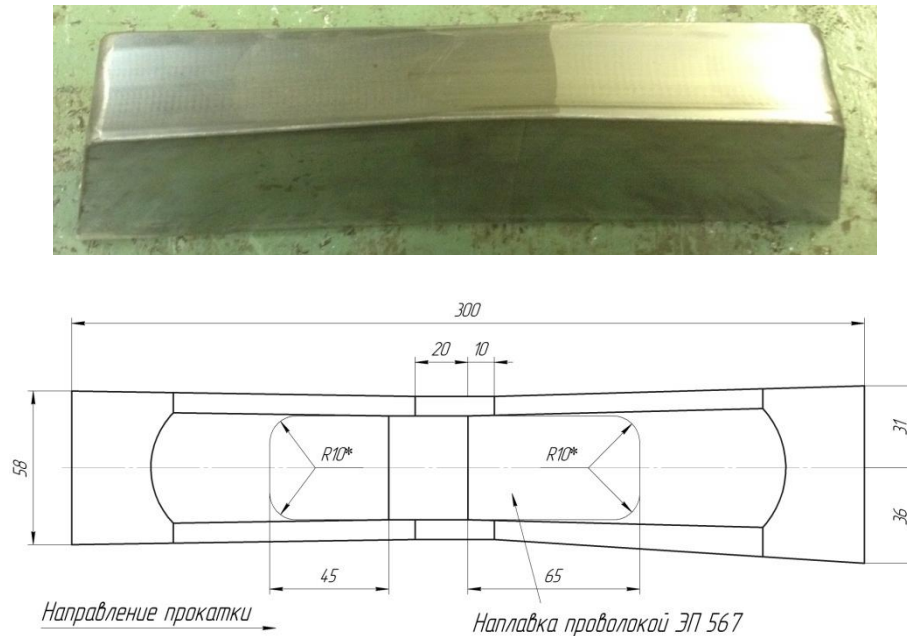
Направляющие линейки для прошивки заготовок диаметром 65 мм
